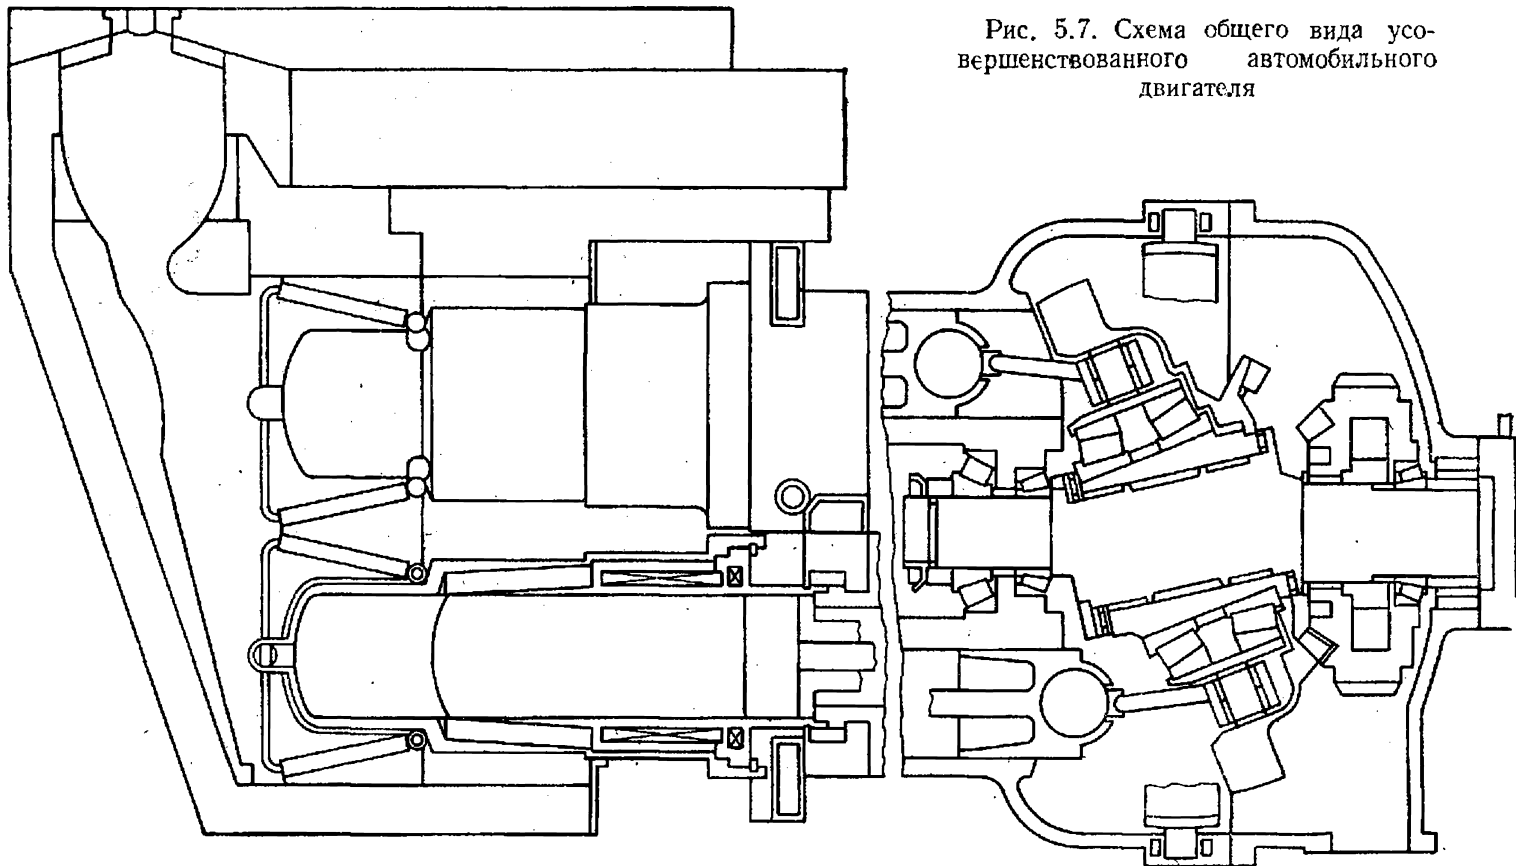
Схема общего вида усовершенствованного автомобильного двигателя
